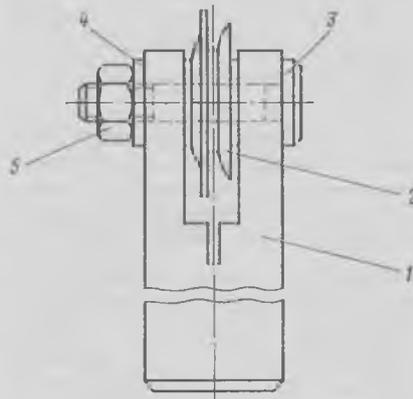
Приспособление для закатки гребешков в канавки вала ротора:
